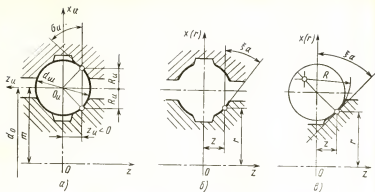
Параметры профиля винта и гайки шариковинтовой пары
